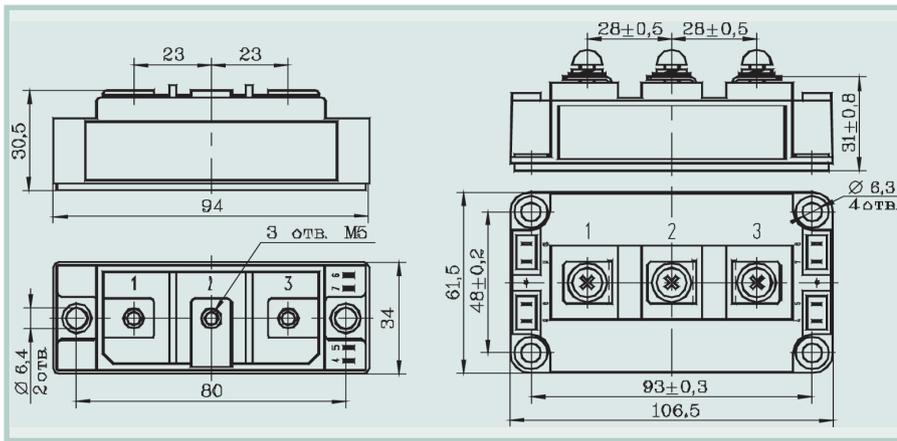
Чертёж силовых IGBT-модулей паяной конструкции стандарта 34 и 62 мм
